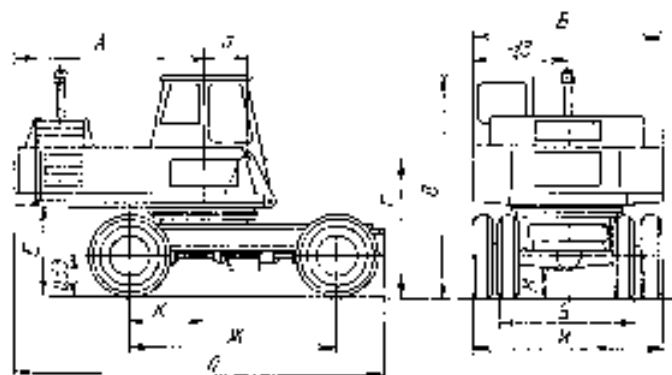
Габаритные размеры пневмоколесных подпоповоротных экскаваторов
